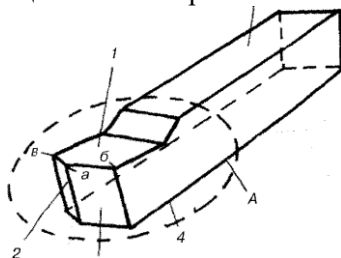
Резец и его элементы: A — рабочая часть, B - тело резца; 1 - передняя поверхность; 2 - вспомогательная поверхность; 3 - главная поверхность; 4 - основание; ab - главная режущая кромка; av - вспомогательная режущая кромка
